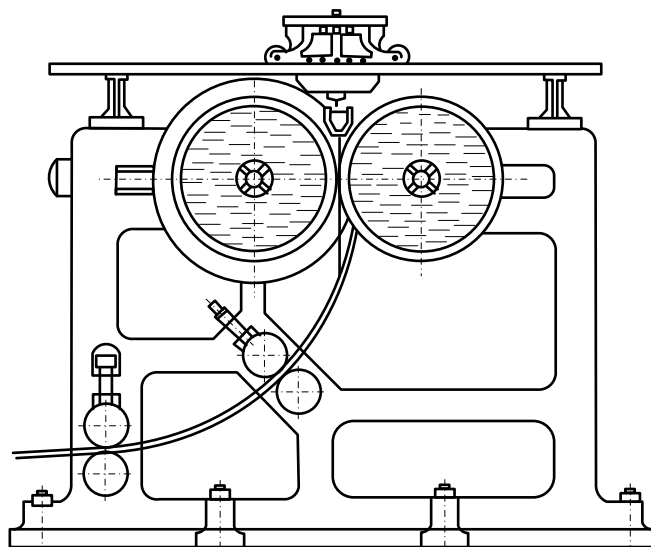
Установка непрерывной разливки («бесслитковой прокатки») конструкции Г. Бессемера
